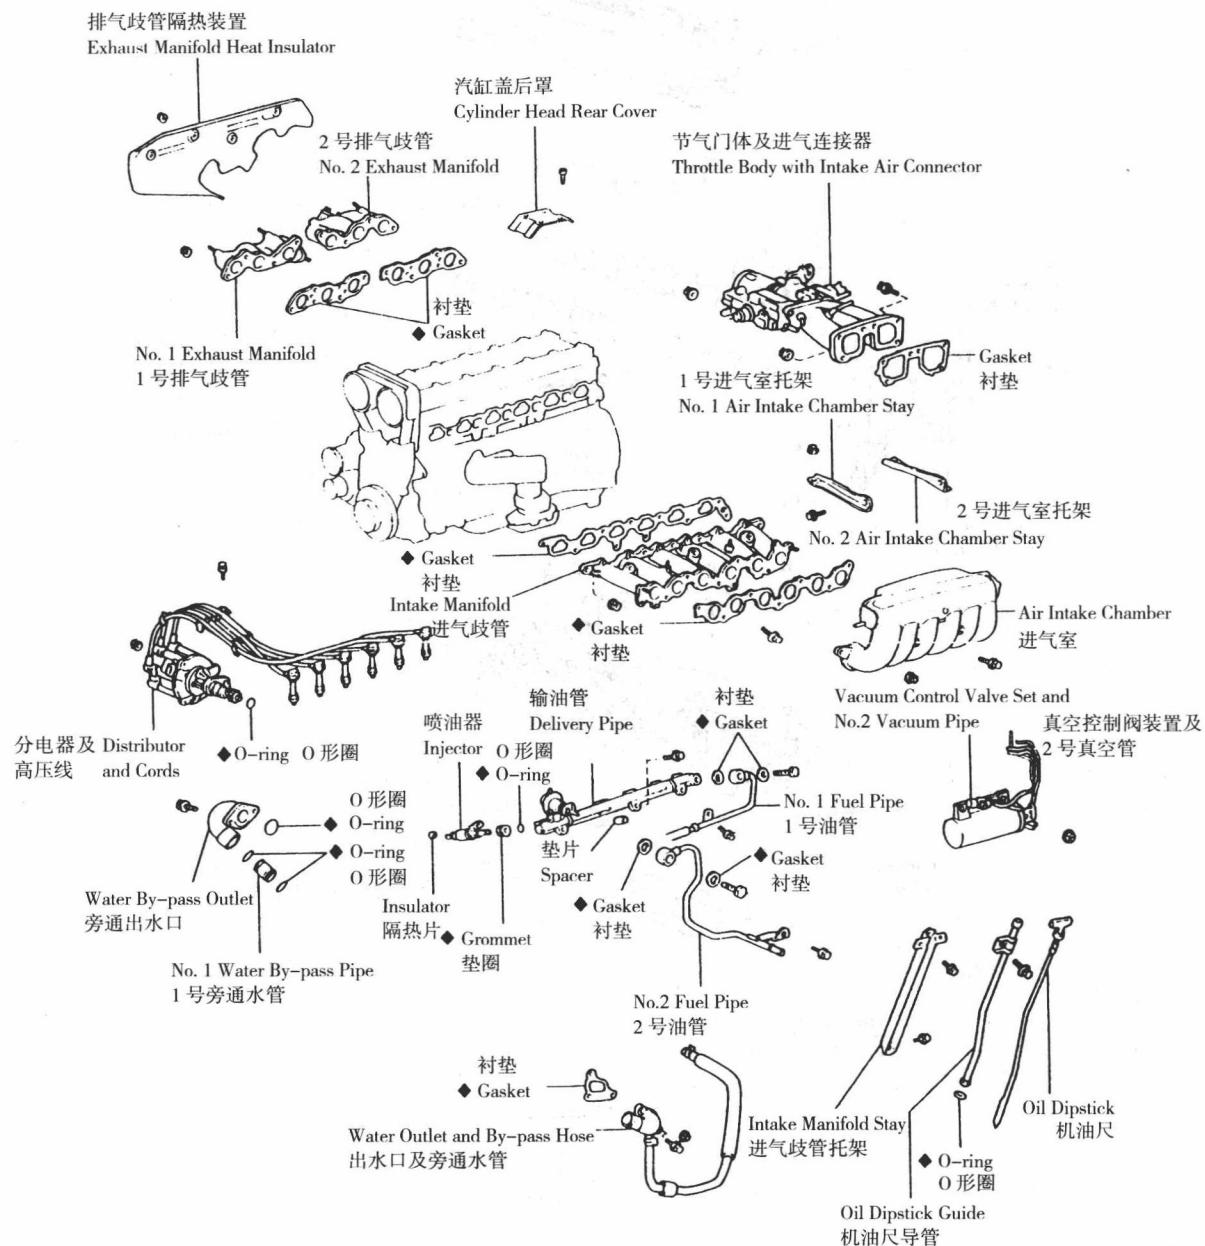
汽缸盖 (CYLINDER HEAD) (1)
